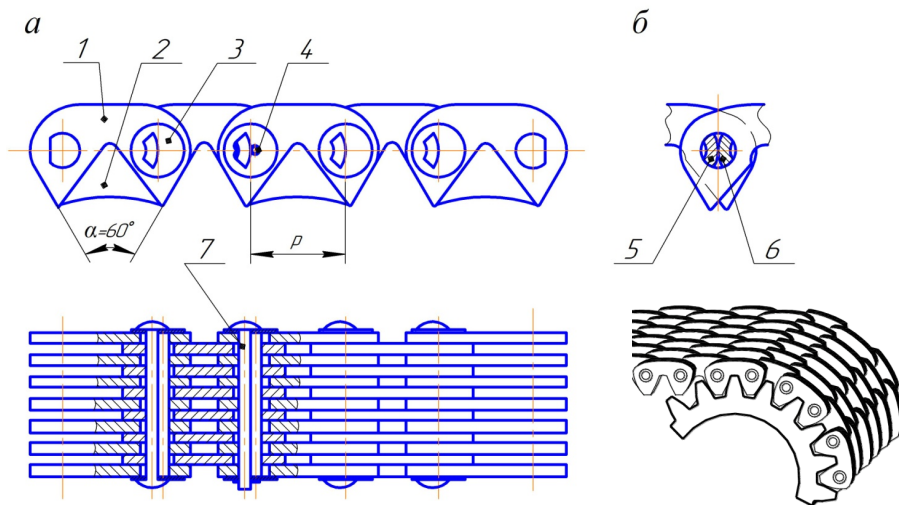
Зубчатая приводная цепь (а) и шарнир качения (б):
